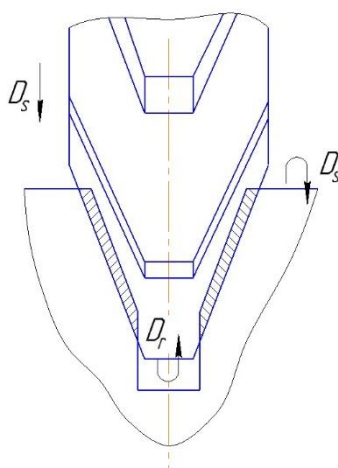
Обработка боковых поверхностей ручьев фасонной дисковой фрезой
